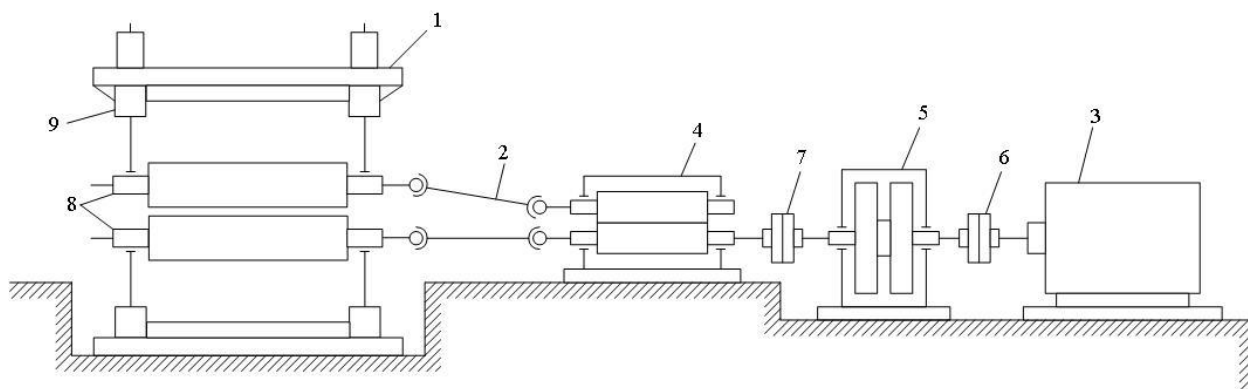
Схема главной линии рабочей клетки: 1 – главная рабочая клетка; 2 – универсальные шпиндели; 3 – главный электродвигатель; 4 – шестерённая клетка; 5 - редуктор; 6 – моторная муфта; 7 – зубчатая муфта; 8 – рабочие валки; 9 – станины
